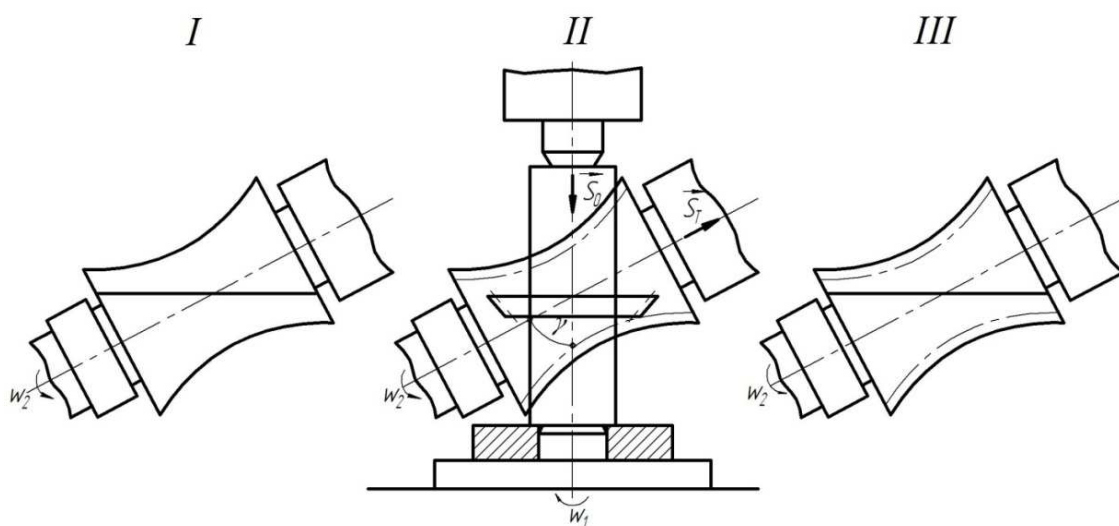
Схема изготовления гиперболических зубчатых колес
